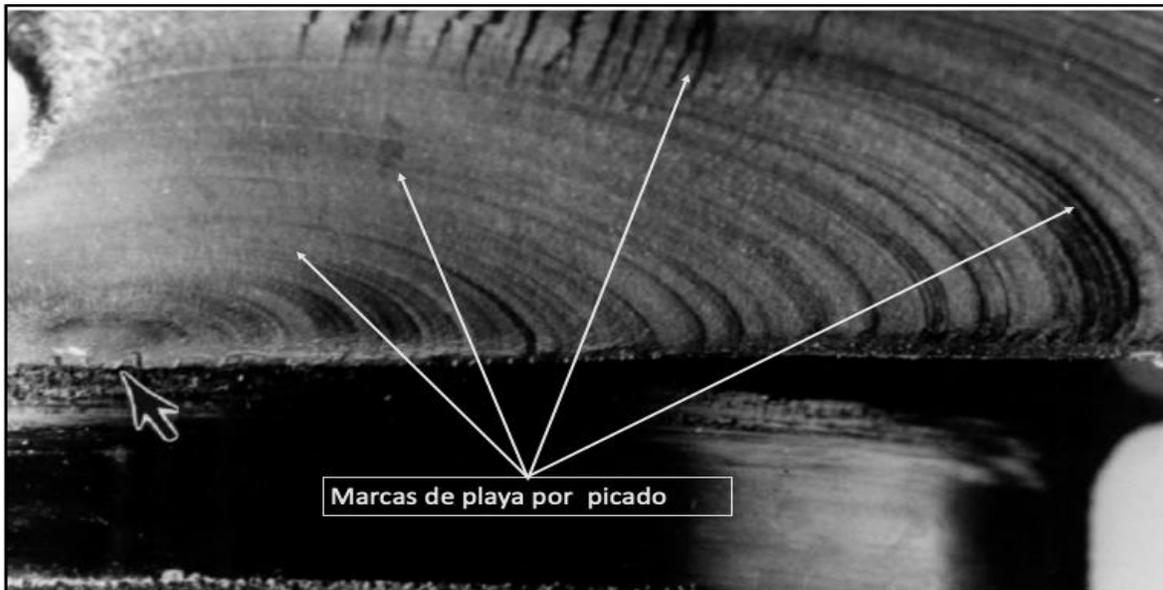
Fisuras encontradas sobre el muñón del cigüeñal.
